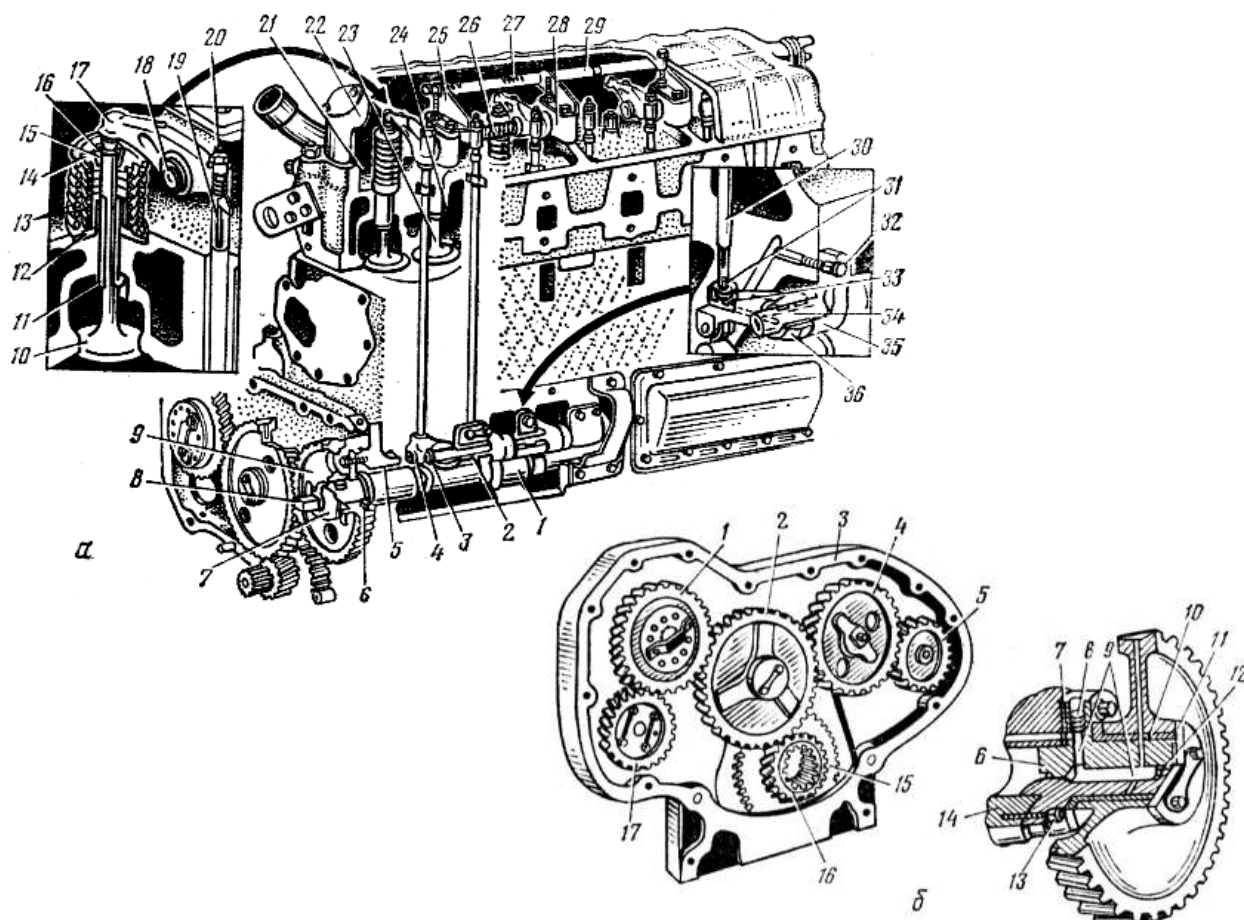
Газораспределительный механизм двигателя А-41:
